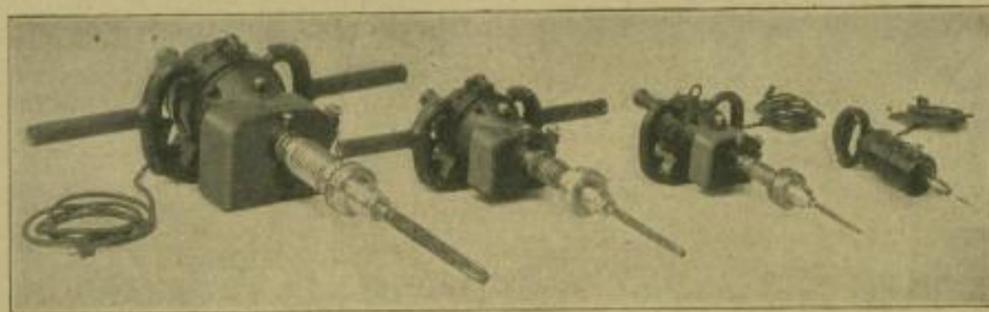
Gewindeschneidmaschinen mit bügelförmigen Handgriffen und Umschalter
